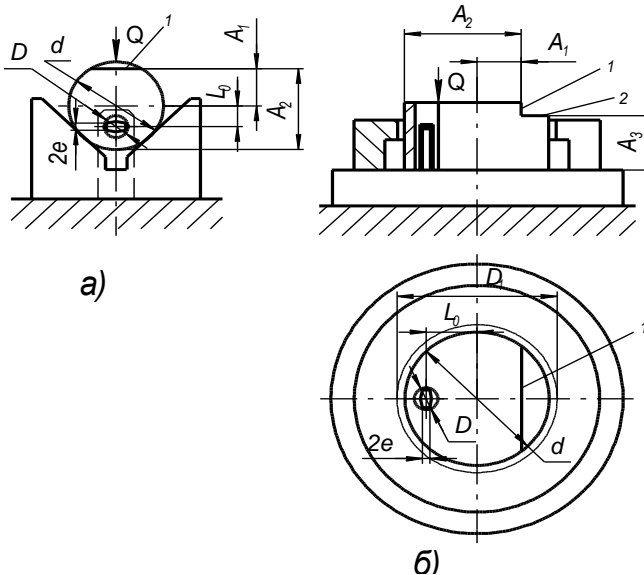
Варіанти схем встановлення заготовки при фрезеруванні паза (до задачі 10).
